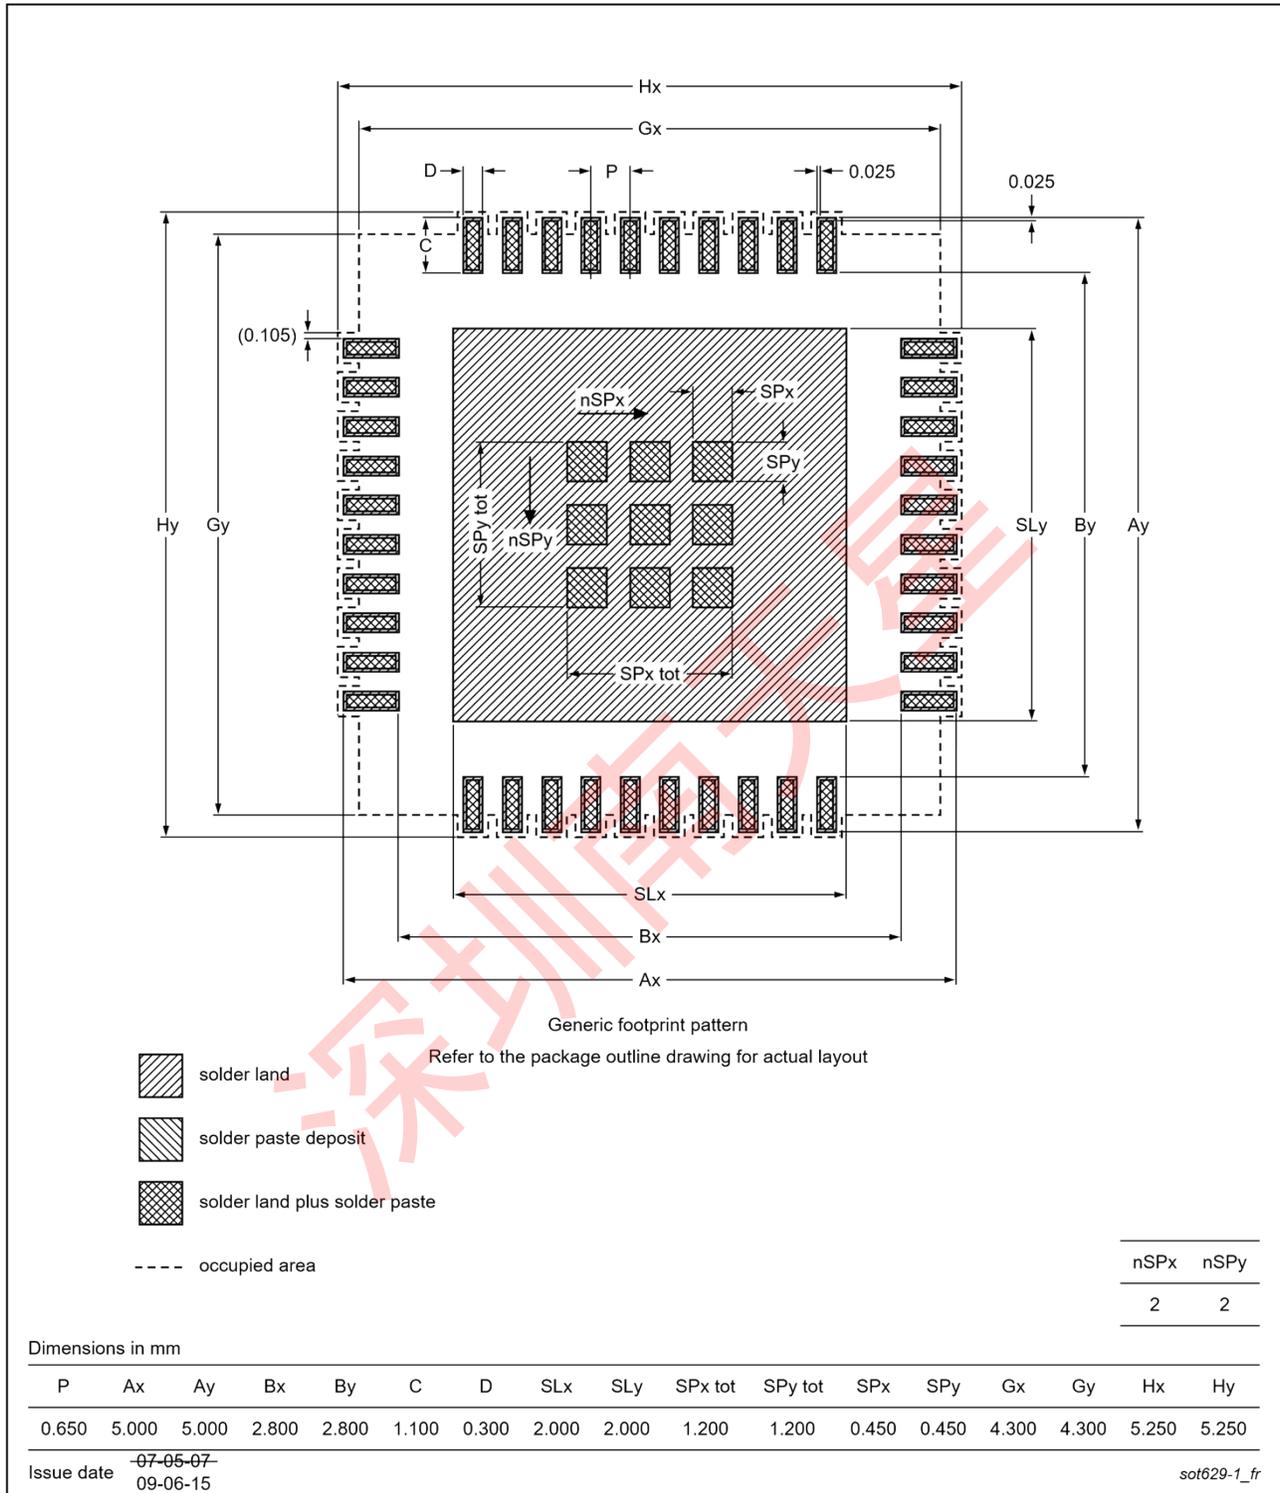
SOT629-1 (HVQFN16) 的 PCB 占地面积; 回流 soldering
